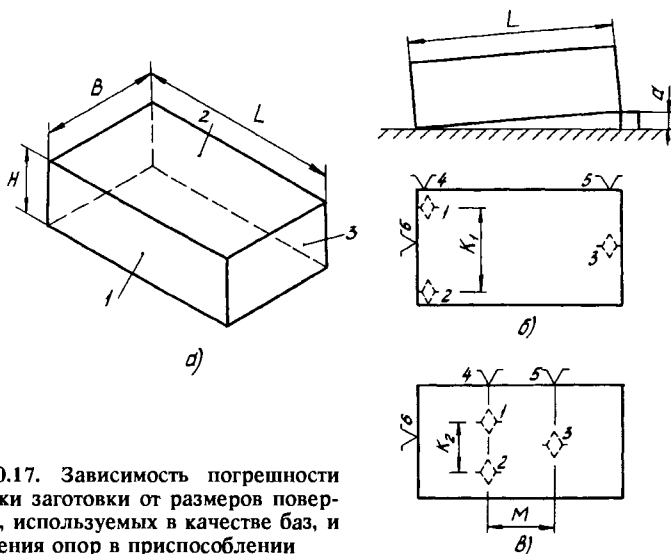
Зависимость погрешности установки заготовки от размеров поверхностей, используемых в качестве баз, и размещения опор в приспособлении
